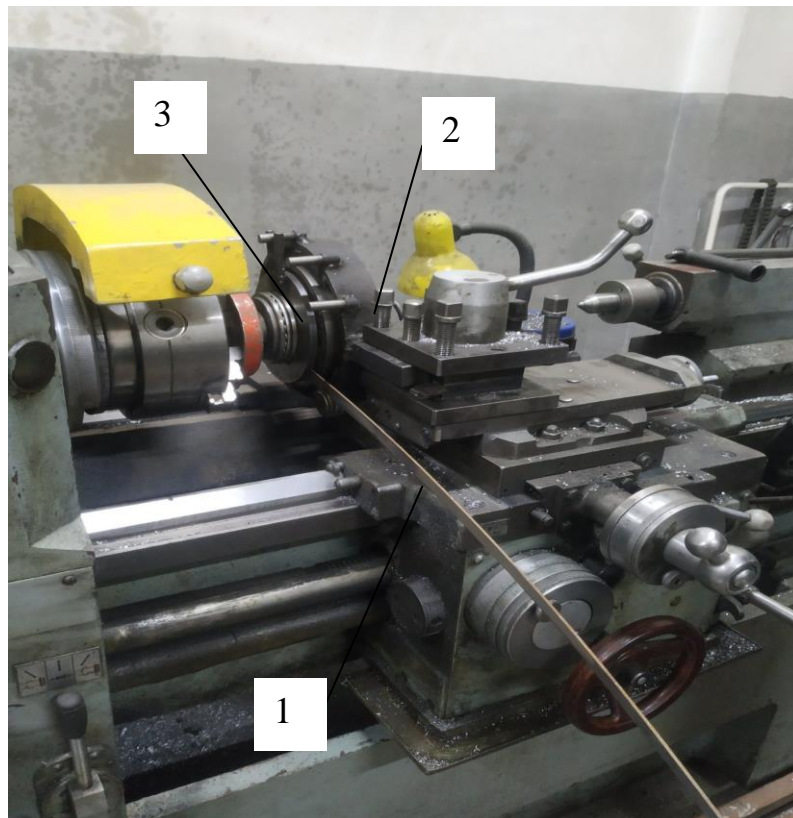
Загальний вигляд експериментальної установки для технологічного процесу навивання гвинтової заготовки з обертовою втулкою: 1 - стрічка для навивання; 2 – гвинтова заготовка; 3 - пристрій для навивання
